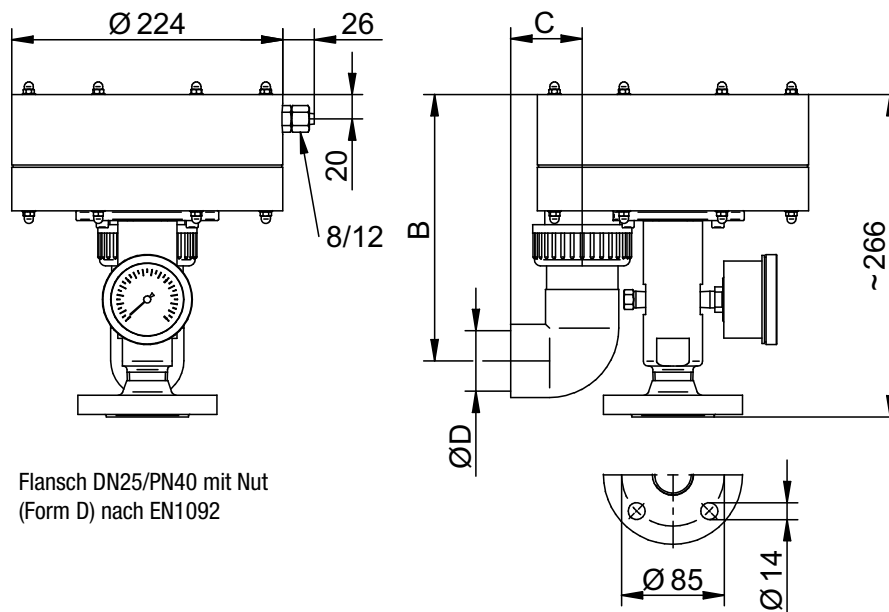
Maßbild Vakuumregler mit Gewindeanschluss
